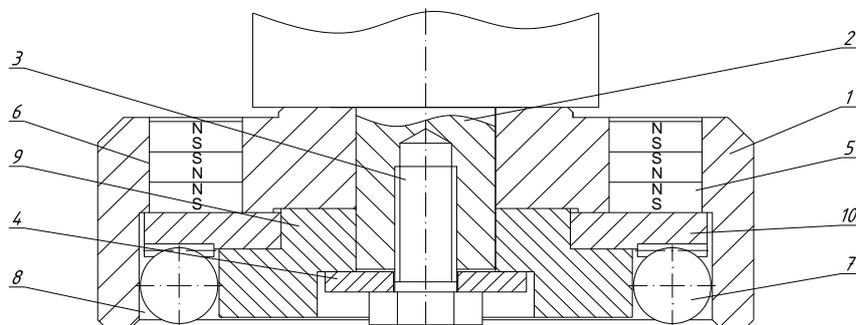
Однорядный инструмент для упрочнения плоских поверхностей
